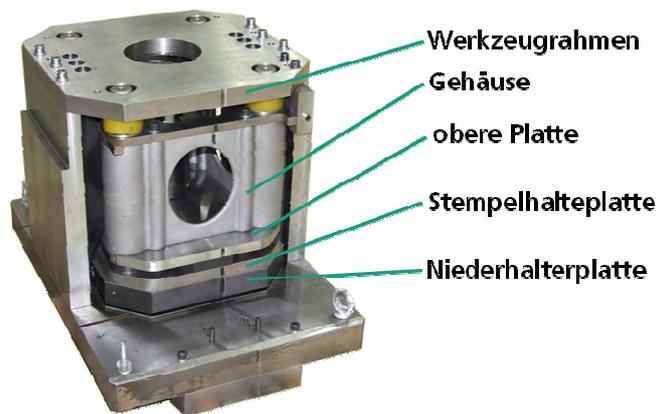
Werkzeug zum Schneiden von Blechteilen
